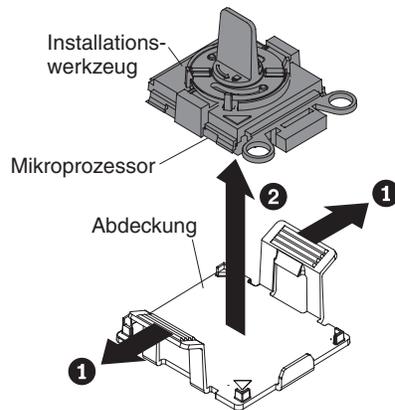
Abdeckung am Installationswerkzeug entfernen
